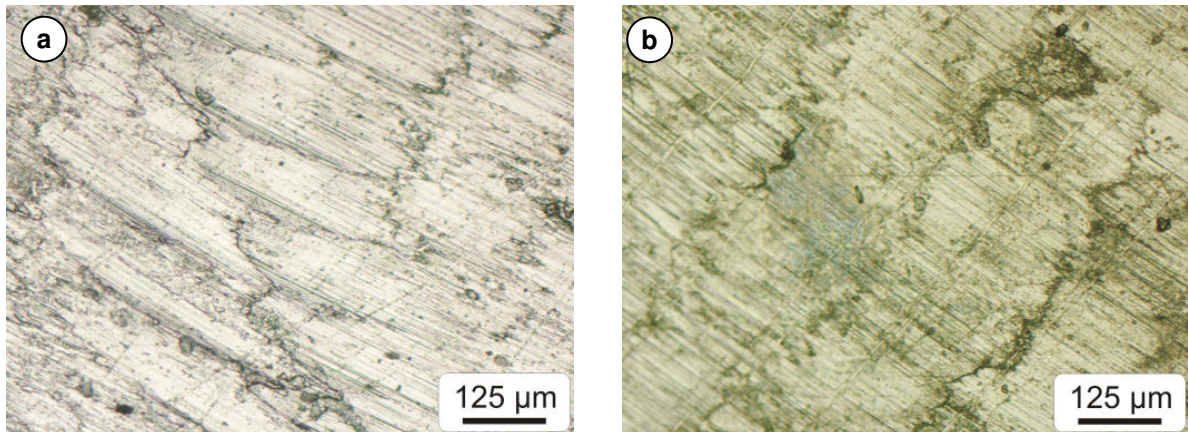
Aufsicht auf Oberflächen von Werkstücken nach Bearbeitung mit 400 m/min
